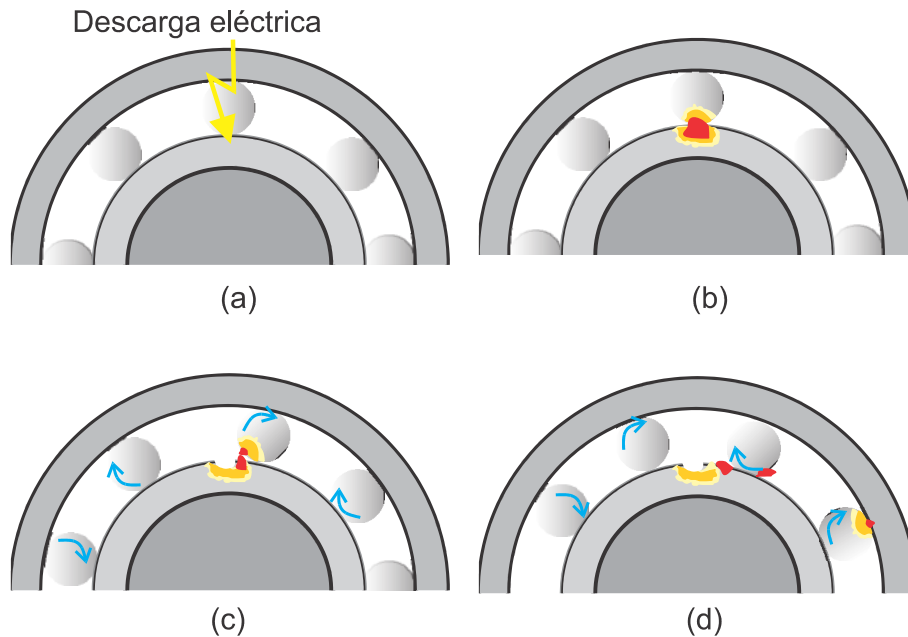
Arco eléctrico en un rodamiento metálico: (a) La corriente eléctrica pasa a través de los elementos rodantes. (b) La soldadura por arco se produce entre los elementos rodantes y la pista del rodamiento. (c) El material fundido se solidifica y separa. (d) El exceso de material se elimina debido a la rotación de los elementos rodantes (Zamudio-Ramirez et al., 2021).
